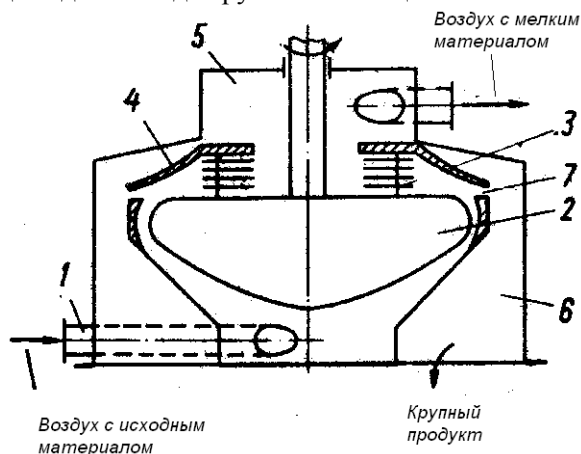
Схема центробежного классификатора с вращающейся зоной разделения: 1 – входной патрубок; 2 – вращающееся центральное тело; 3 – пластины; 4 – профилированная крышка; 5 – коллектор сбора мелкого продукта; 6 – коллектор сбора крупного продукта; 7 – поверхность вывода крупного продукта.
